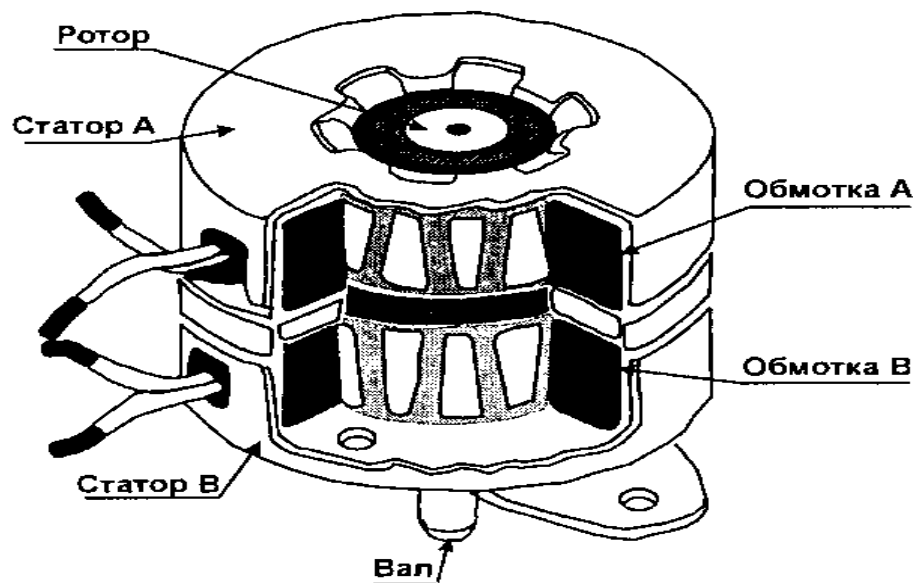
Конструкція біполярного крокового двигуна
